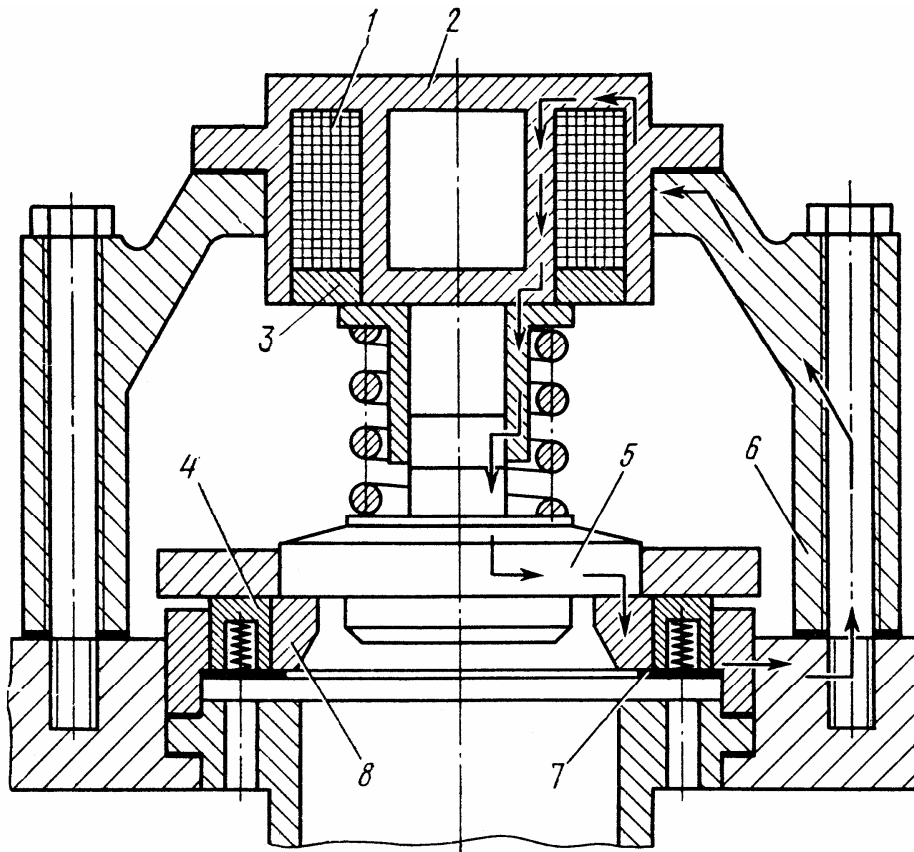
Схема електромагнітного віджиму пластини всмоктувального клапана: 1 – котушка електромагніта; 2 – корпус електромагніта; 3, 4 – немагнітні вставки; 5 – нагнітальний клапан; 6 – проставка компресора; 7 – пластинка всмоктувального клапана; 8 – корпус всмоктувального клапана
